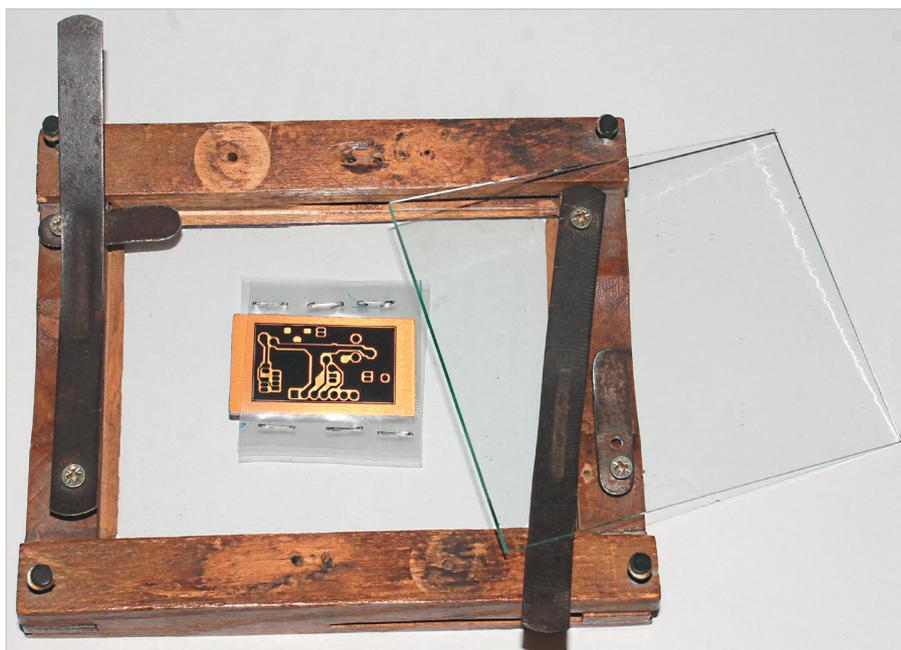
Рамка для контактной печати снимков с фотопластинок и плоских плёнок формата 9×12 см
